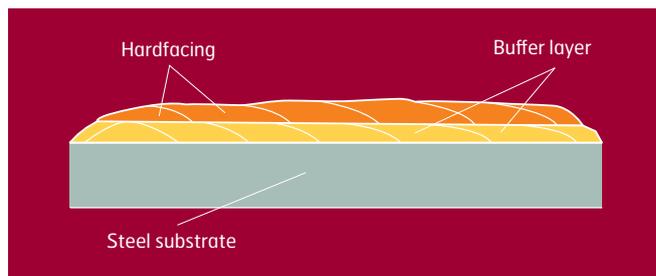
Ejemplo de secuencia de soldadura para capa de 'búfer' (capa amortiguadora) y revestimiento de soldadura con metal duro
